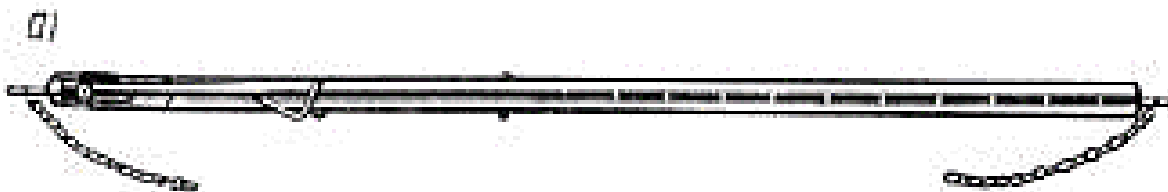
Линейка для проверки схождения передних колес автомобилей мод. 2182
